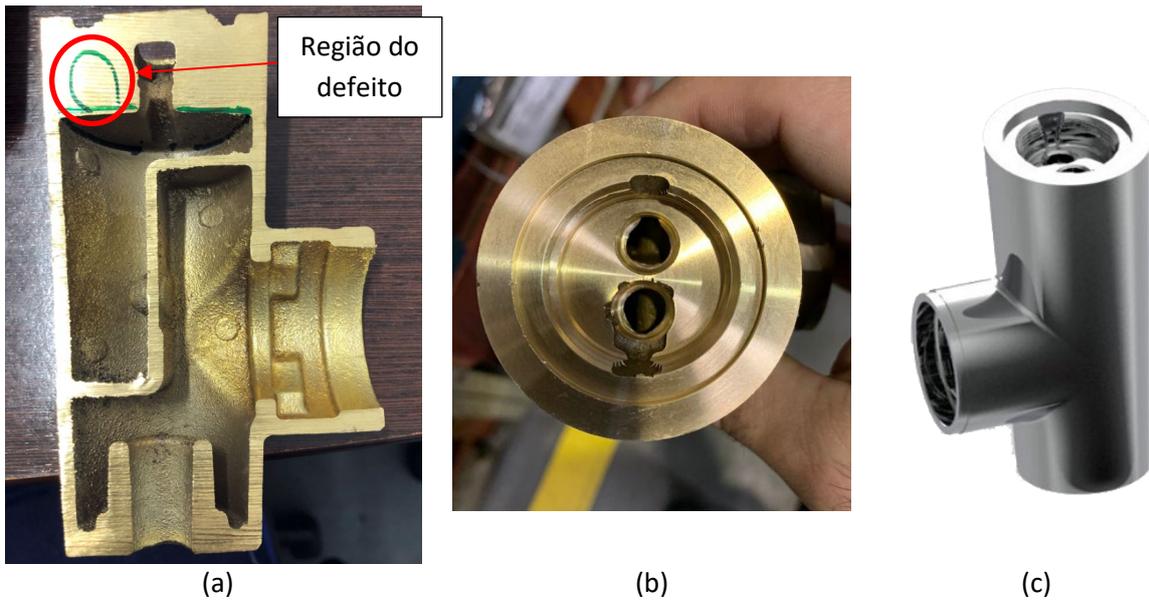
"Choice" (a) área do defeito (b) vista superior após usinagem e (c) componente liberado
